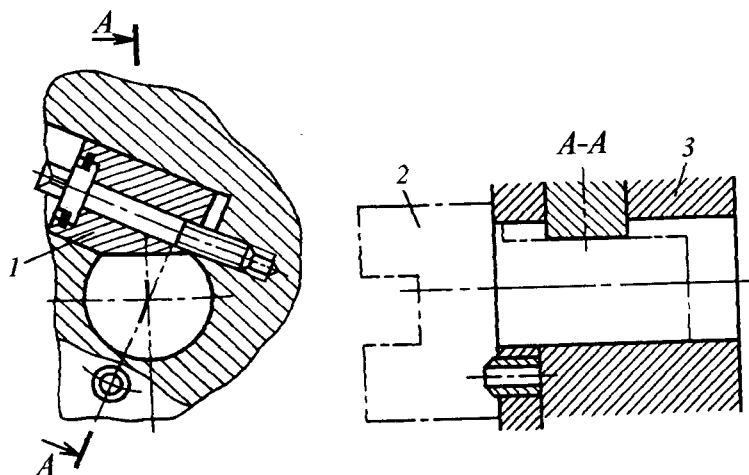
Закрепление резцедержателя в револьверной головке
